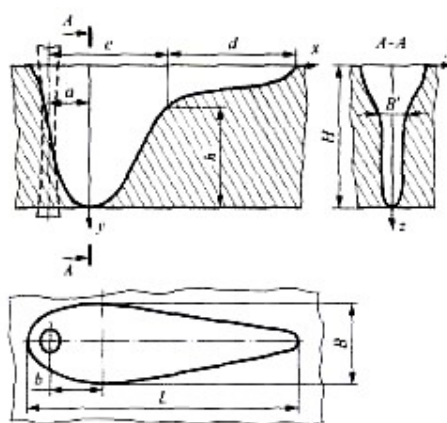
Форма сварочной ванны при лазерной сварке
